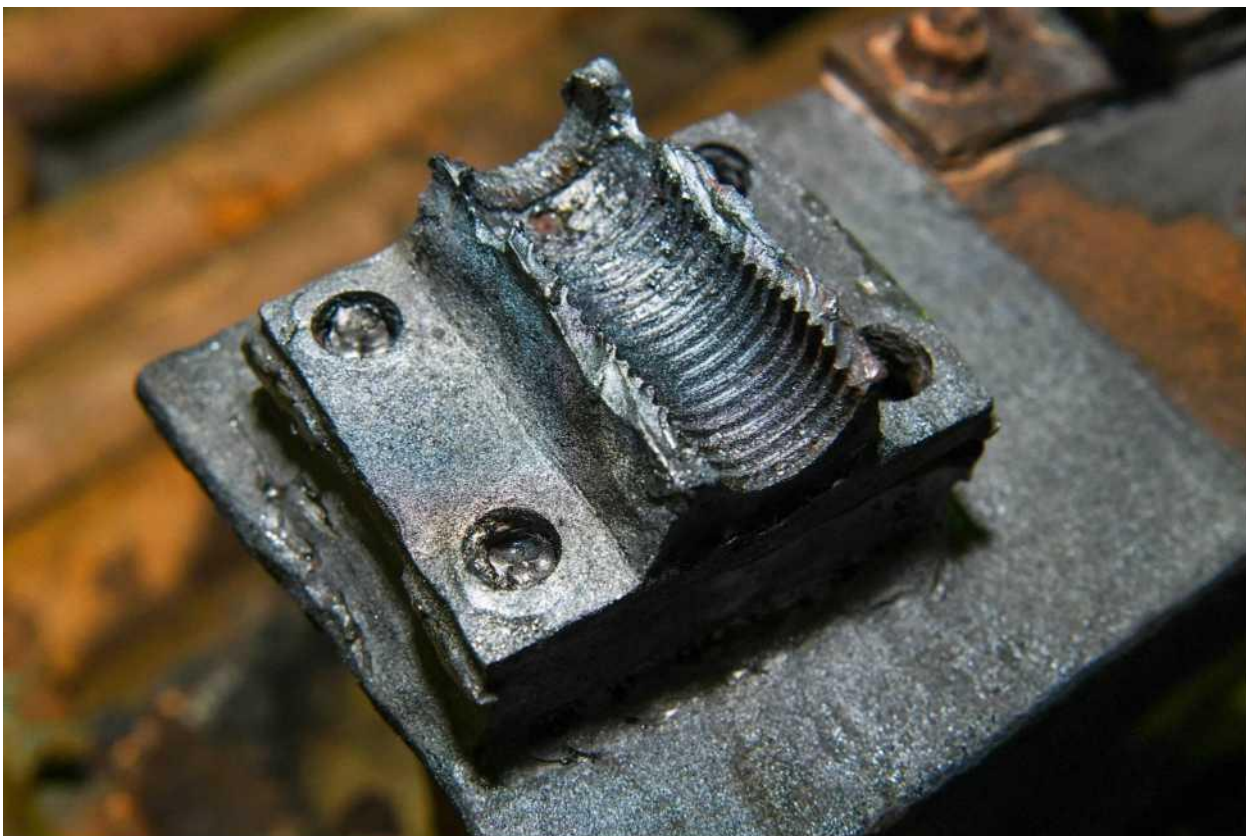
Результат обработки Исходный образец - металлоконструкция. Материал СТЗ. Обрабатываемая поверхность - язвенная коррозия.
